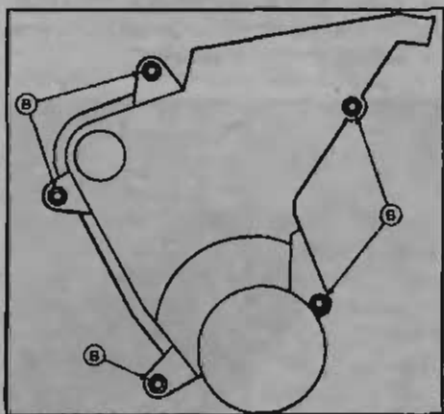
Расположение болтов крепления нижнего зубчатого ремня
